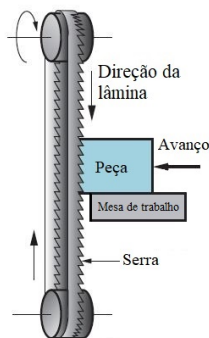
Operação de corte com serrote de fita vertical (Adaptado de [5]).
